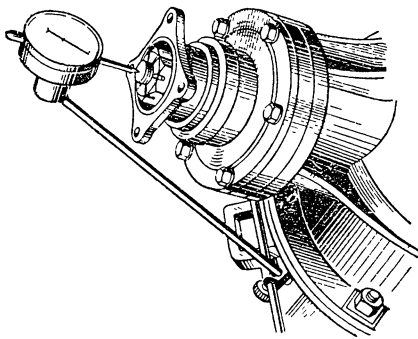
Определение осевого люфта в подшипниках ведущей шестерни главной передачи индикатором
